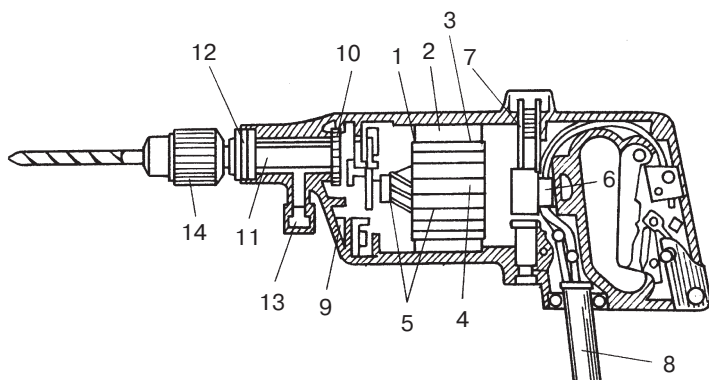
Электродрель: 1 — электродвигатель; 2 — сердечник электромагнита; 3 — башмаки электромагнита; 4 — якорь; 5 — обмотка якоря; 6 — коллектор; 7 — щетки; 8 — ввод тока; 9 — вал якоря; 10 — зубчатая передача; 11 — шпиндель дрели; 12 — шарикоподшипник; 13 — масленка; 14 — патрон дрели
